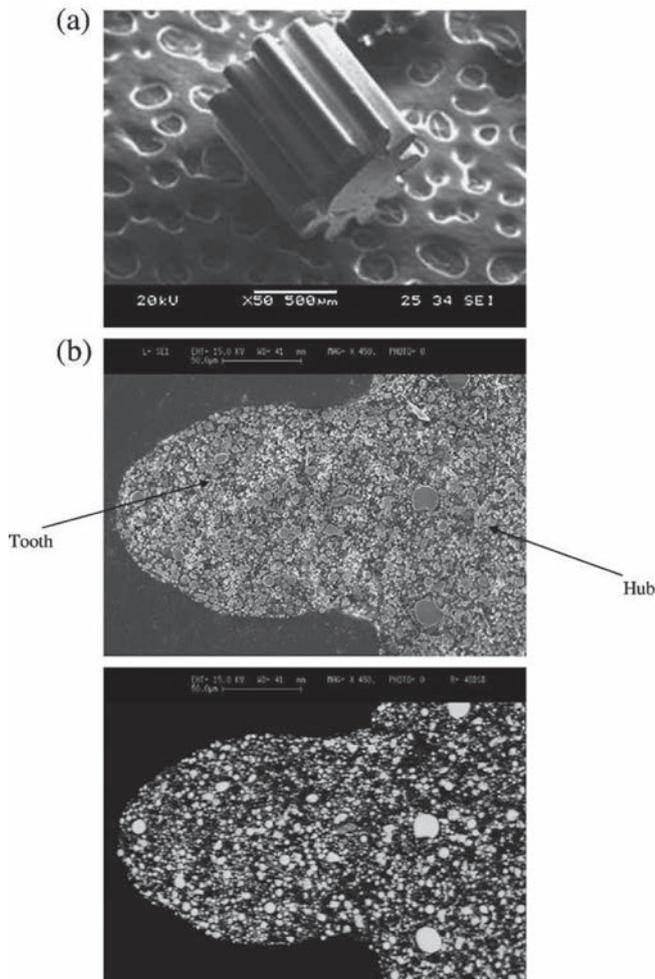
(a) Micro engrenagem, (b) Distribuição do Pó, centro e periferia do dente; [15].
